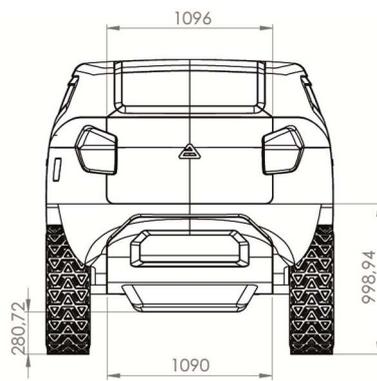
Vista posterior. Escala 1/50; dimensões em milímetros. Fonte: autor.
